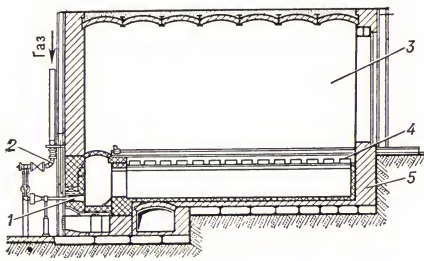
Камерное сушило для литейных форм и стержней на газовом отоплении: 1 — газовая горелка; 2 — газовые коммуникации; 3 — камера сушики; 4 — распределительное устройство; 5 — футеровка.
